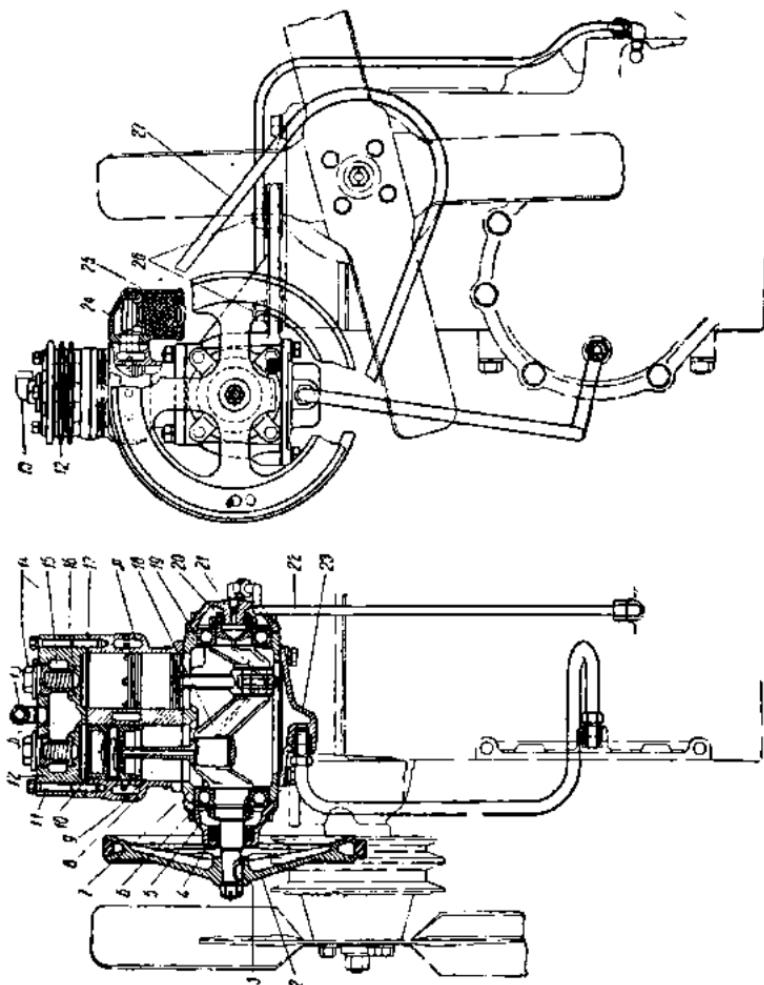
Воздушный компрессор тормозной системы. 1 — трубопровод отвода масла; 2 — головка цилиндров компрессора; 3 — штицер нагнетательного трубопровода; 4 — пробка выпускного клапана; 5 — пружина выпускного клапана; 6 — выпускной клапан; 7 — камера подвода наружного воздуха; 8 — крышка со штицером подвода смазки к компрессору; 9 — трубопровод подвода масла; 10 — зазор между головкой цилиндра и крышкой; 11 — крышка цилиндра; 12 — головка цилиндра; 13 — штицер нагнетательного трубопровода; 14 — пробка выпускного клапана; 15 — пружина выпускного клапана; 16 — выпускной клапан; 17 — крышка со штицером подвода смазки к компрессору; 18 — трубопровод подвода масла; 19 — зазор между головкой цилиндра и крышкой; 20 — крышка цилиндра; 21 — крышка со штицером подвода смазки к компрессору; 22 — трубопровод подвода масла; 23 — зазор между головкой цилиндра и крышкой; 24 — крышка цилиндра; 25 — кронштейн крепления к головке блока двигателя; 26 — кронштейн крепления к головке цилиндра.
